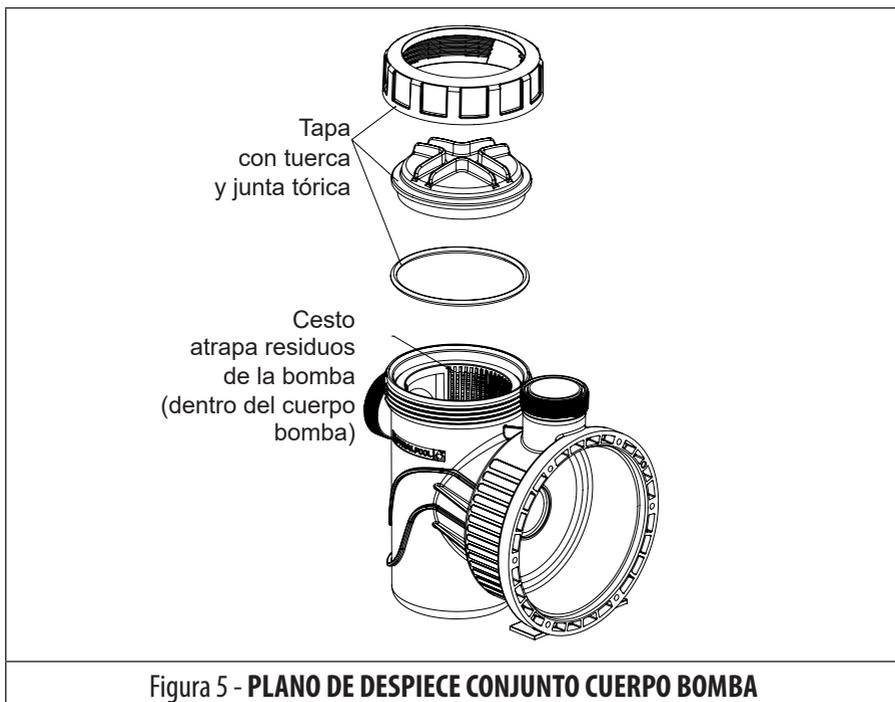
PLANO DE DESPIECE CONJUNTO CUERPO BOMBA
